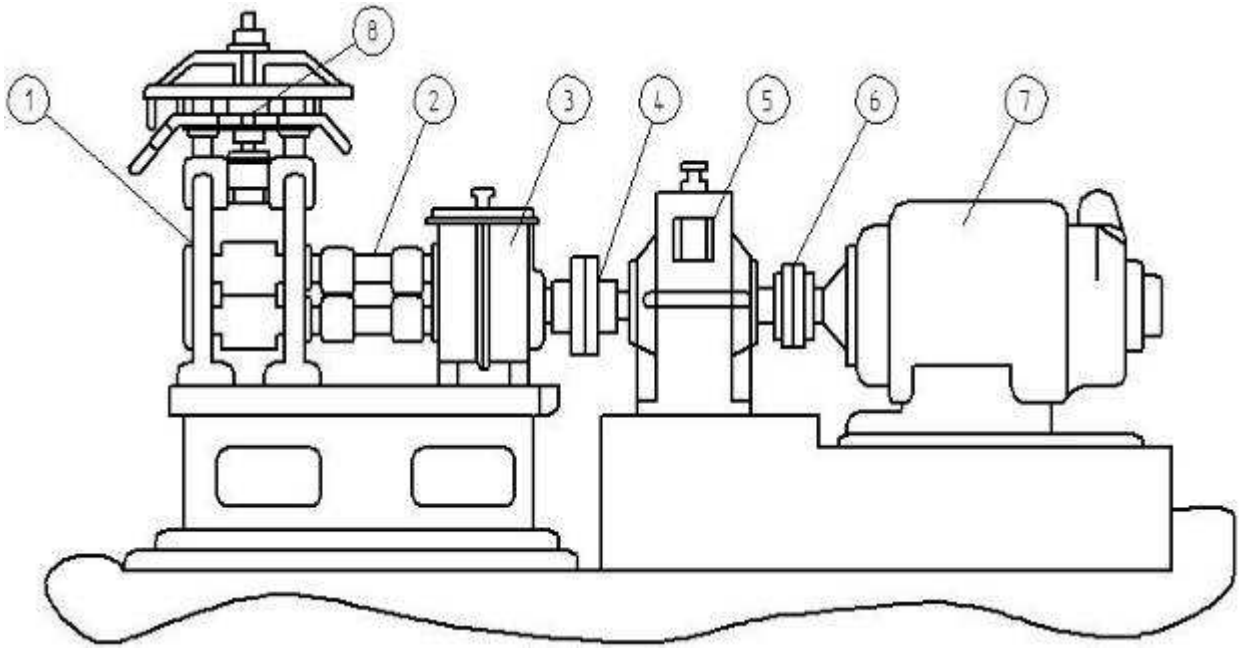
Схема розташування обладнання лабораторного стану 180 кафедри ОМТ ДДТУ
